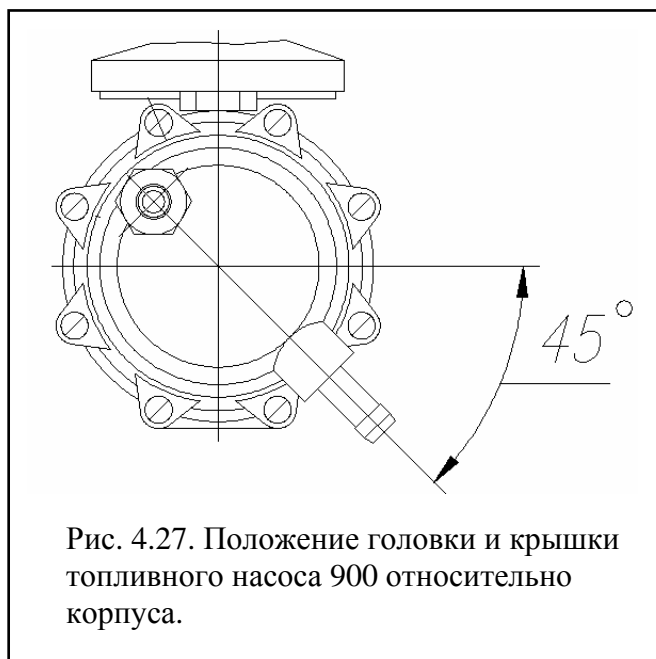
Положение головки и крышки топливного насоса 900 относительно корпуса.
